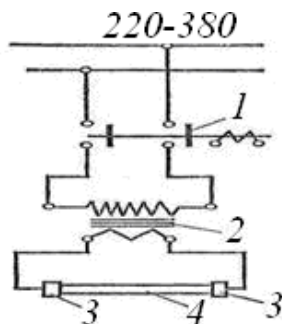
Схема електроконтактного нагрівання заготовки: 1 – контактор; 2 – трансформатор; 3 – контактні головки; 4 – заготовка
